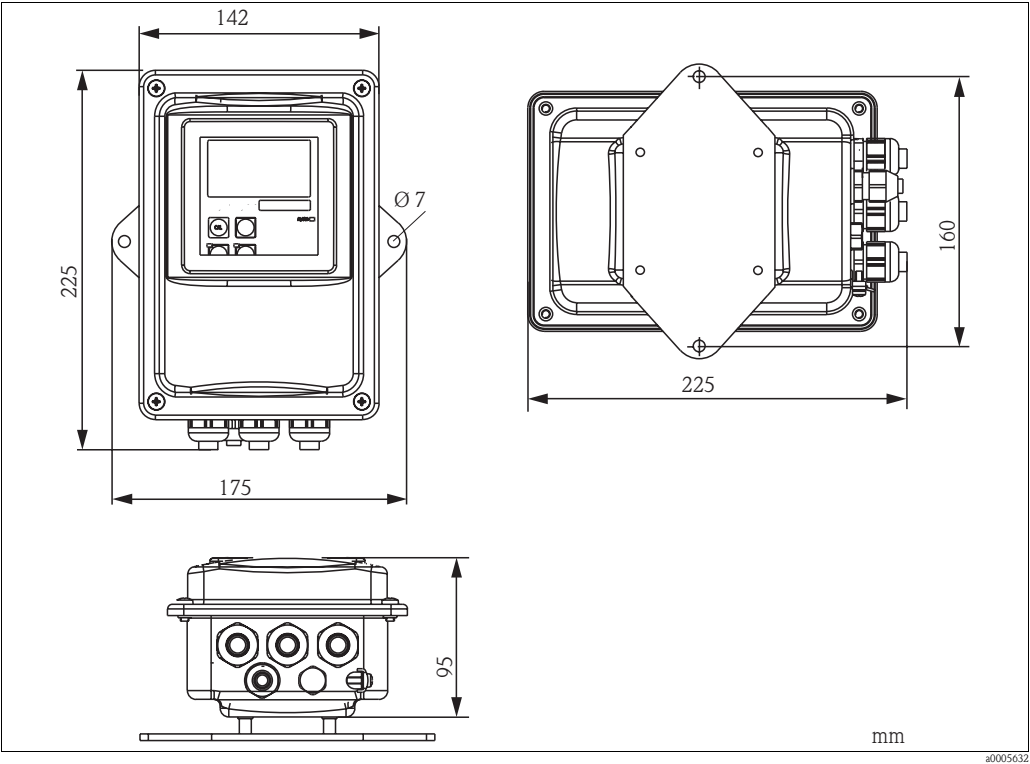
Montaje del CLD134 en una pared utilizando la placa de montaje
